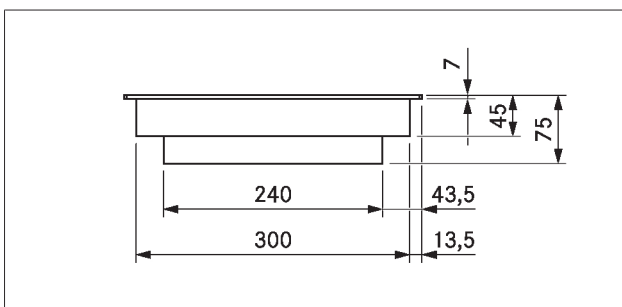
Dimensões do aparelho CKCH, vista frontal
